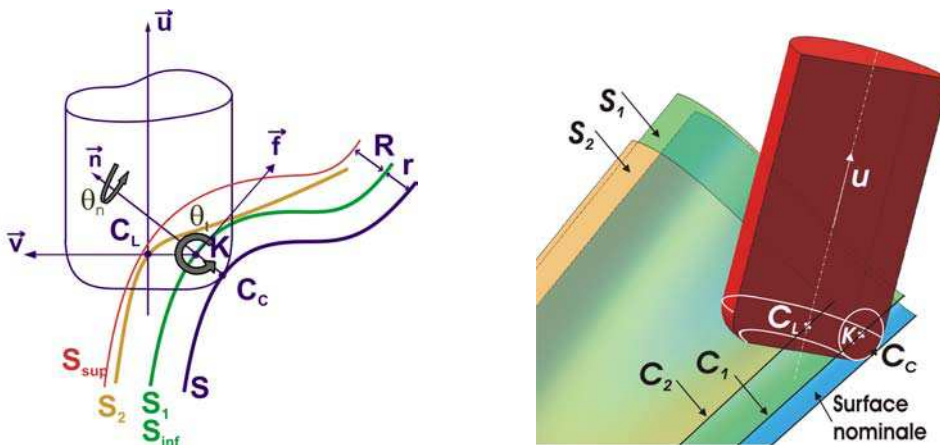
la surface d'usinage en fraisage à 5 axes avec un outil torique
